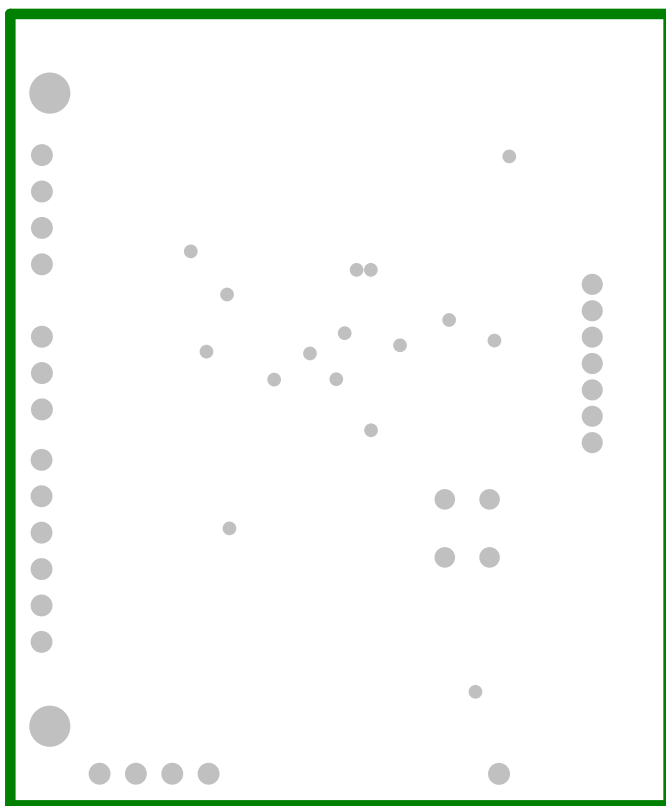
ADS124S18EVM PCB 布局 - 内部接地 (GND) 层 1
